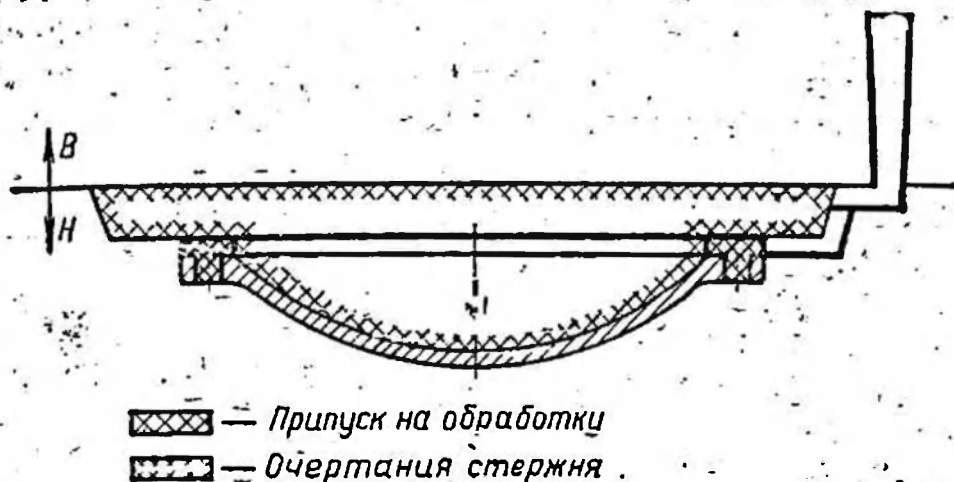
Отливка с припусками для механической обработки и с технологическими припусками для образования формовочных уклонов.
